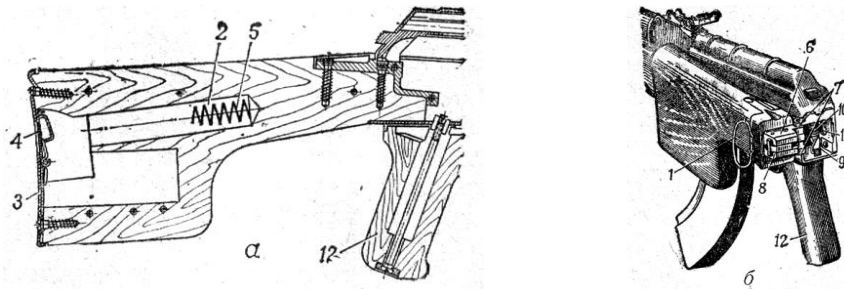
Приклад и pistolетная рукоятка пулемета:
